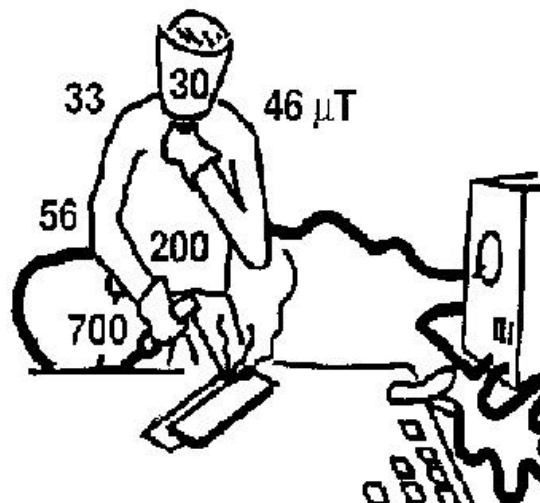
Valores de los campos magnéticos que afectan al soldador durante el proceso de soldadura manual con electrodo revestido (SMAW)
